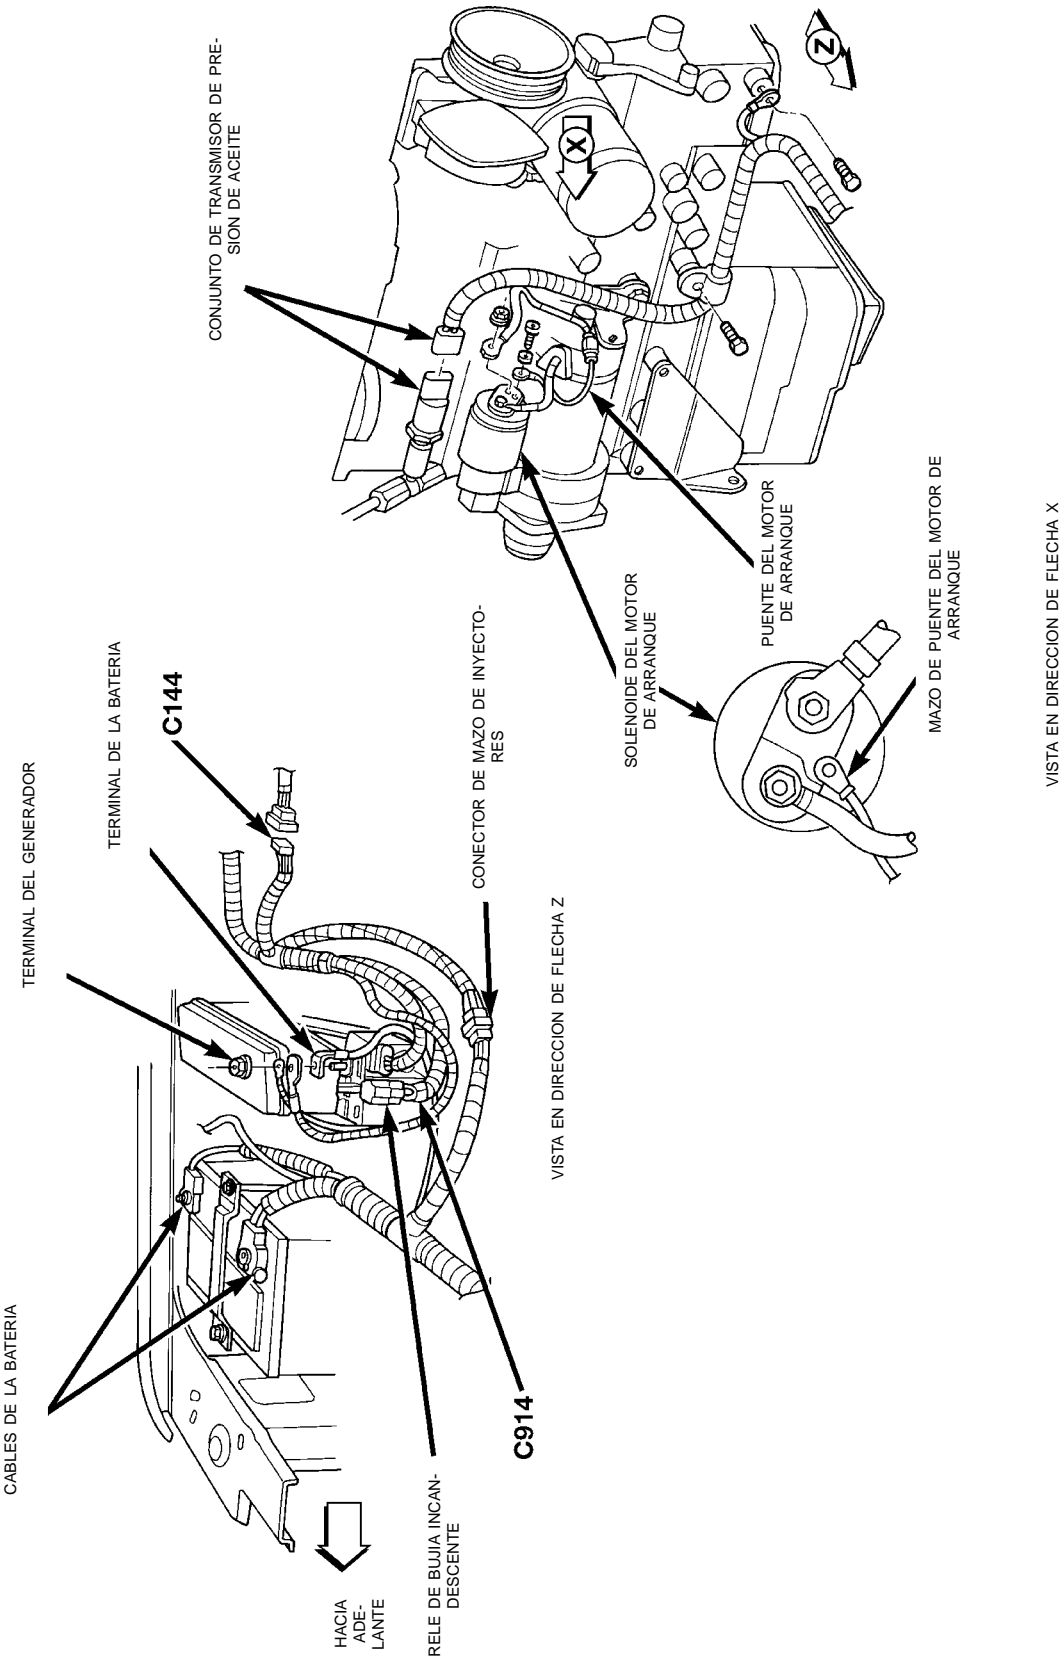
Conectores de la batería y el motor de arranque—Motor diesel
